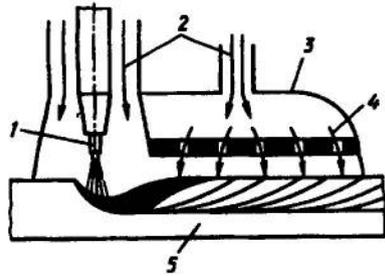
Пальник з подовженою насадкою для механізованого зварювання:
